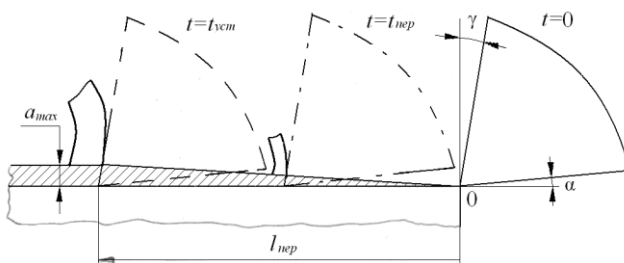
Схема переходного процесса при встречном цилиндрическом фрезеровании (тип I)
